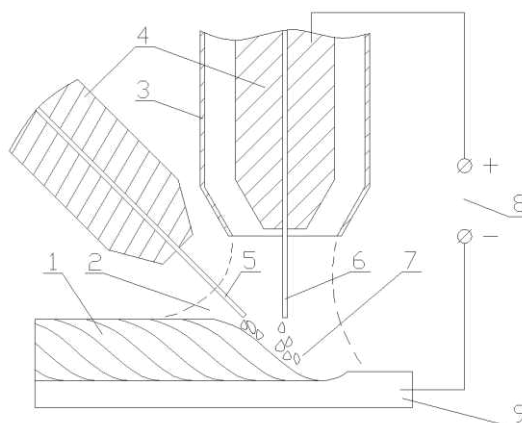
Схема процесса сварки в защитных газах с ДПП:
